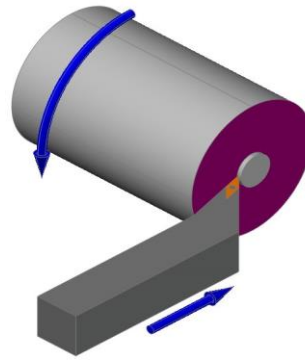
Výroba ve spojení obrábění a 3D tisku [8].
